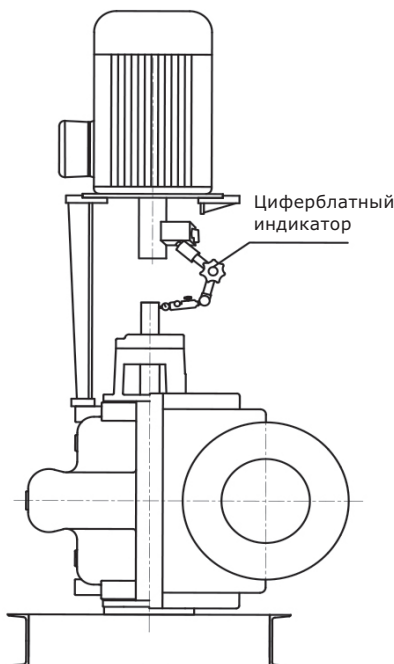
Контроль вертикального смещения, конструкция с упругой втулочно-пальцевой муфтой
